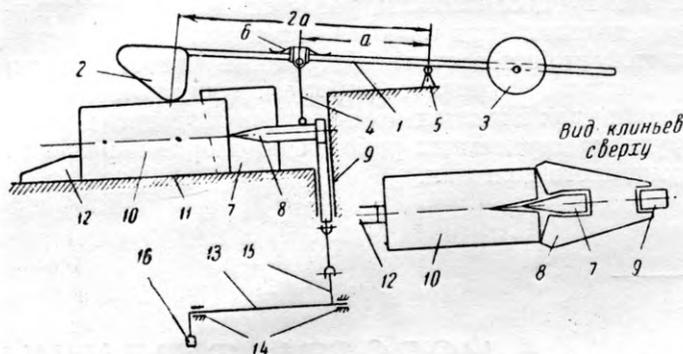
Кинематическая схема установочного устройства и механизма подъема горизонтального клина
